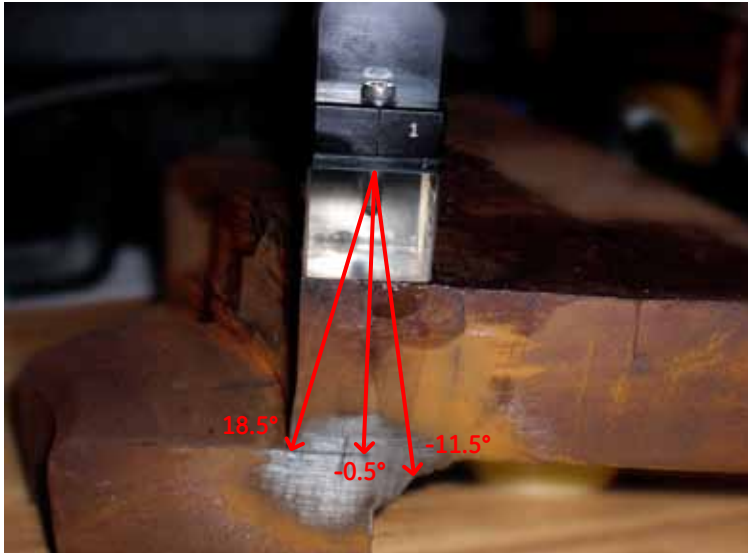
Posición del transductor en el área del final de la penetración de la soldadura.
